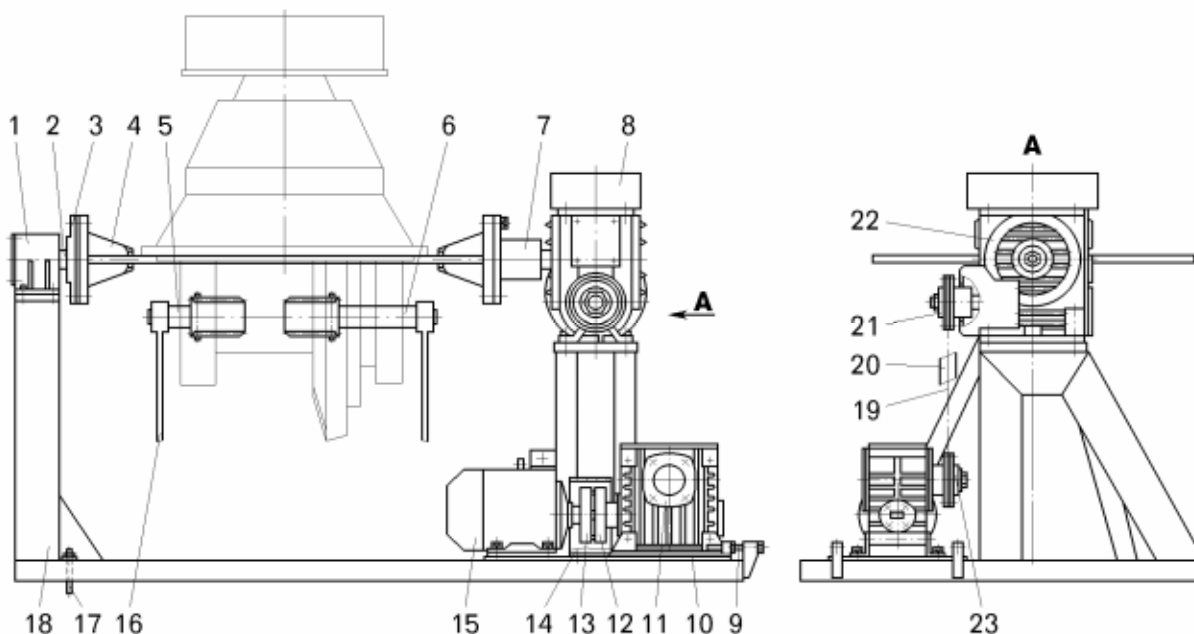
Стенд-кантователь для сборки и разборки главной передачи ведущего моста:
